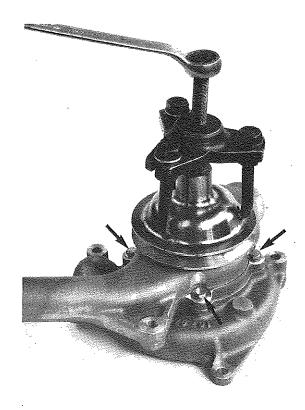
Estrattore n. 19 - Viti fissaggio Puller No. 19 - Screws
